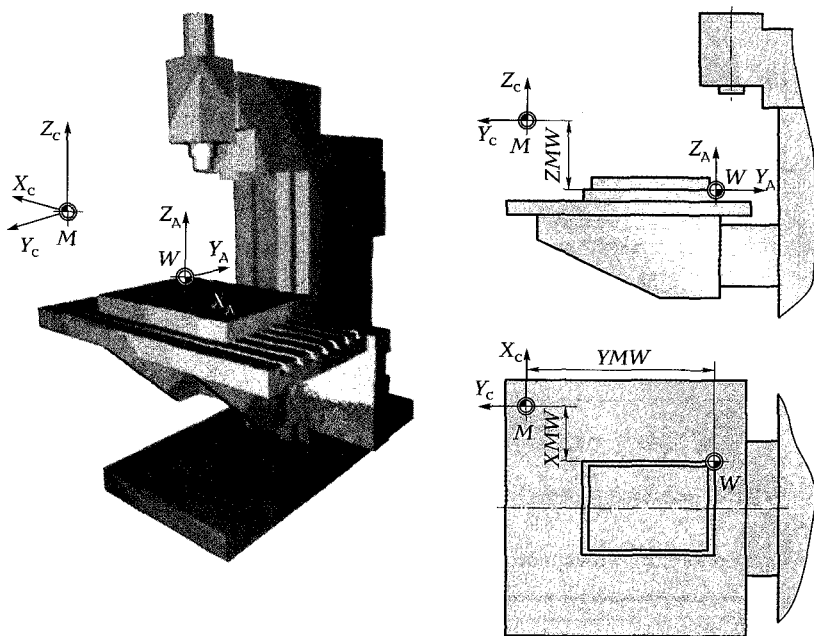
Положение нулевой точки W детали в системе координат фрезерного станка
